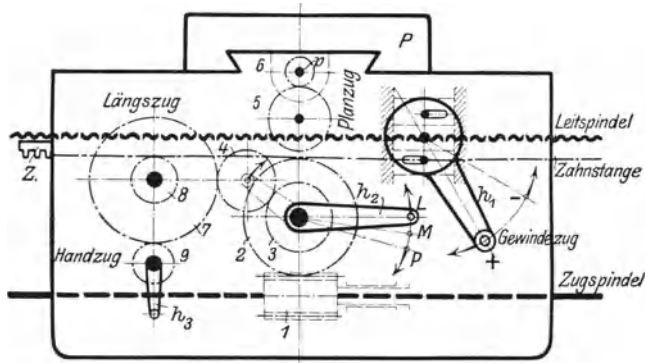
Schloßplatte einer Leit- und Zugspindelbank.
